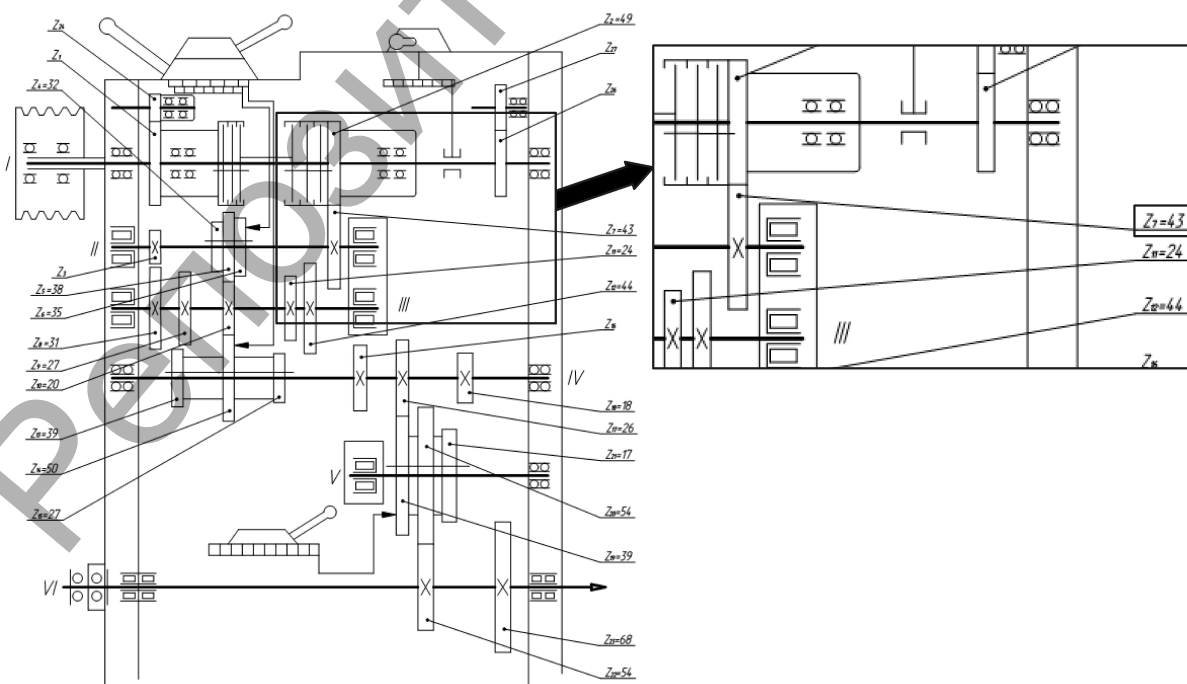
Кинематическая схема коробки скоростей привода главного движения токарного станка SN-501
